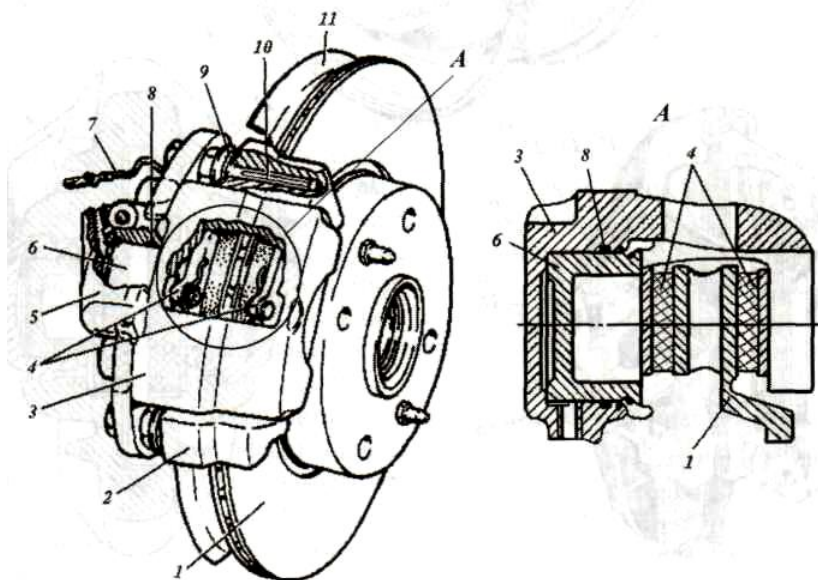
Дисковый тормозной механизм с плавающей скобой:
